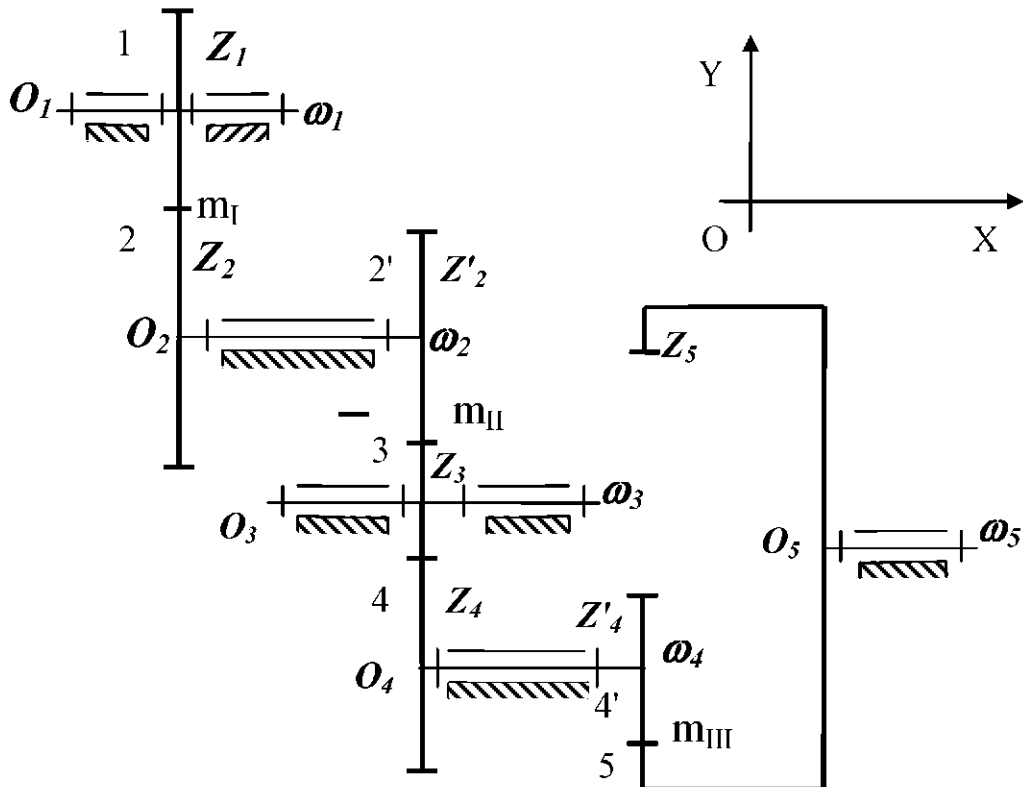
Кинематическая схема МЗМ с неподвижными осями колес
